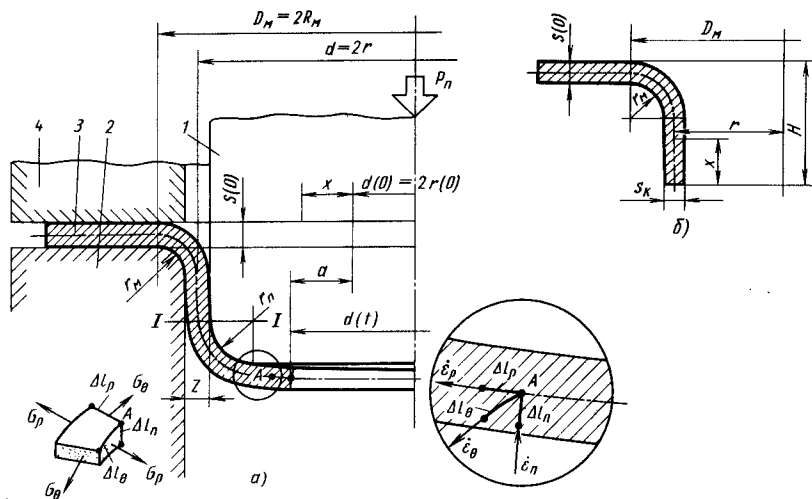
Схема процесса отбортовки (а); форма горловины (б)
